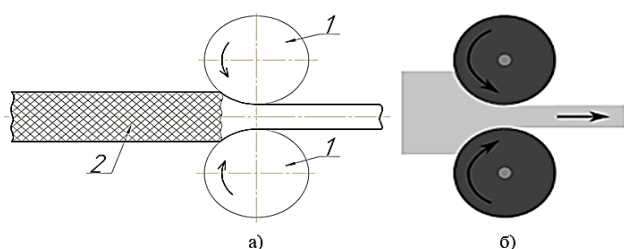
Схематическое изображение (а) и основной процесс пропускания горячего металла между валками, вращающимися в противоположные стороны (б): 1-валки; 2-горячая металлическая полоса (заготовка).
